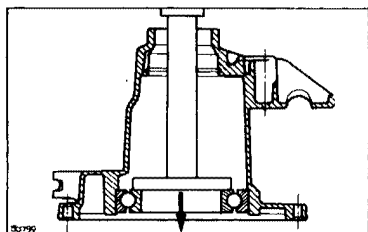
Выпрессовка подшипника ведомой шестерни главной передачи (дифференциала)
